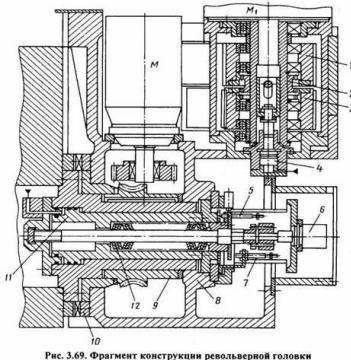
Фрагмент конструкции револьверной головки карусельно-шлифовального станка
